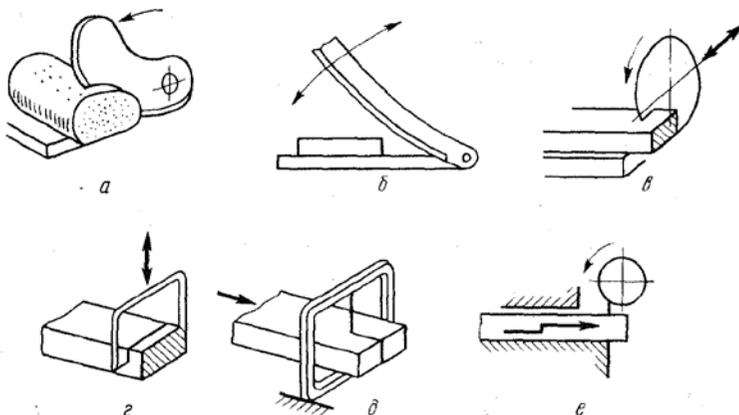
Возможное движение режущего инструмента: а—вращающийся саблеобразный нож, б—качающийся саблеобразный нож, в—вращающийся дисковый нож, г—поступательно движущаяся режущая проволока, д—закрепленная режущая проволока, е—вращающийся нож
